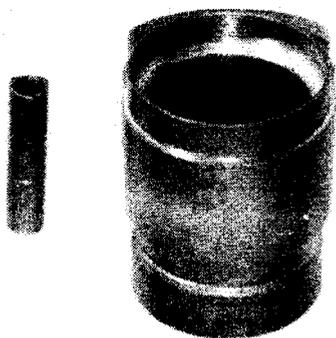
Образцы сварки-пайки меди с коваром (изделия диаметром 50 и 8 мм)
